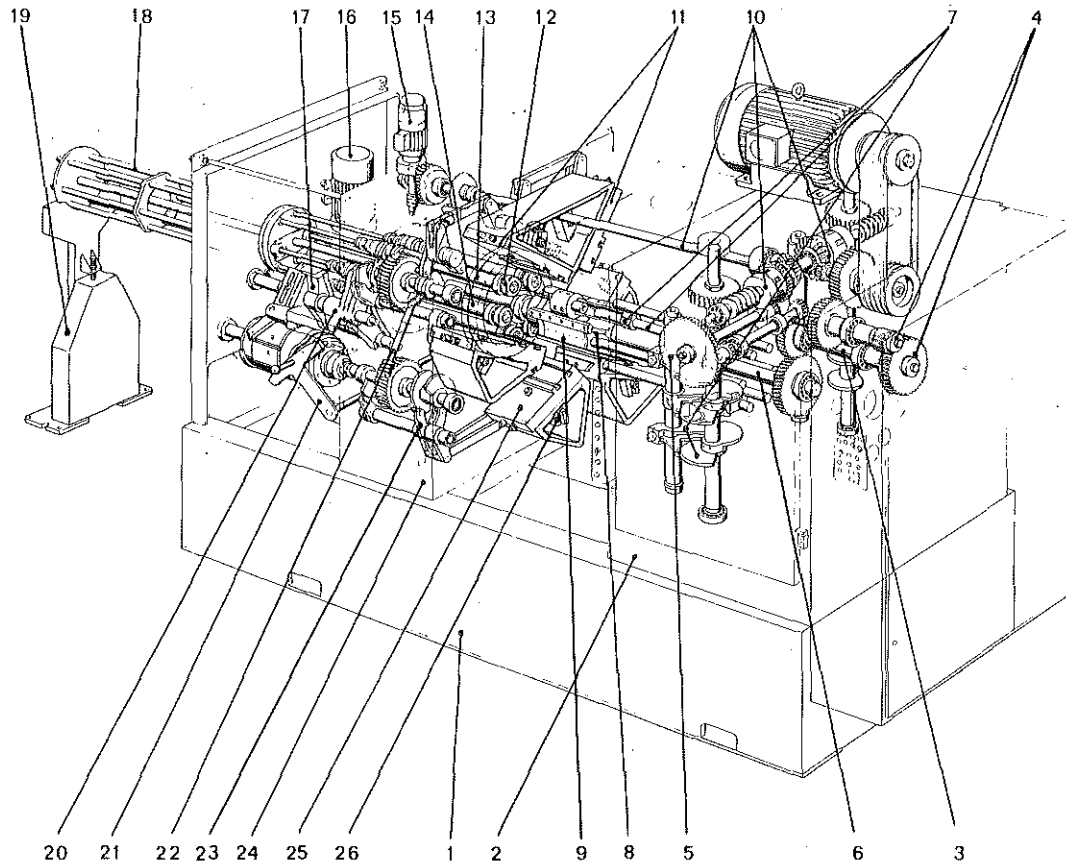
Grundsätzlicher Aufbau des Sechsspindel-Stangenautomaten PS 26/6. 1 Unterkasten, 2 Räderkasten, 3 Schaltschrank, 4 Spindel- und Wechslerräder, 5 Wechslerräder für Stückfolgezeit, 6 Mittelwelle, 7 Längsschlitten-Antrieb, 8 Längsschlittenträger, 9 Kupplungen für Eil- und Arbeitsgang unabhängiger Längsschlitten, 10 Kupplungswelle und Verbindungswelle, 11 oberer Querschlitzen, 12 Drehspindel, 13 Verriegelung mit Stirnzahnkranz, 14 Spindeltrommel, 15 Einrichtmotor, 16 Schmierölpumpe, 17 Vorschubschieber, 18 Stangenführungsrohre, 19 Ständer, 20 Spannschieber, 21 Bedienungshebel für wahlweise Abschaltung des Stangenvorschubs und der Spindeltrommel-Schaltung, 22 Verteilerwelle, 23 Antrieb für unteren Querschlitzen, 24 Spindelkasten, 25 unterer Querschlitzen, 26 Schlittenweg-Verstellung
